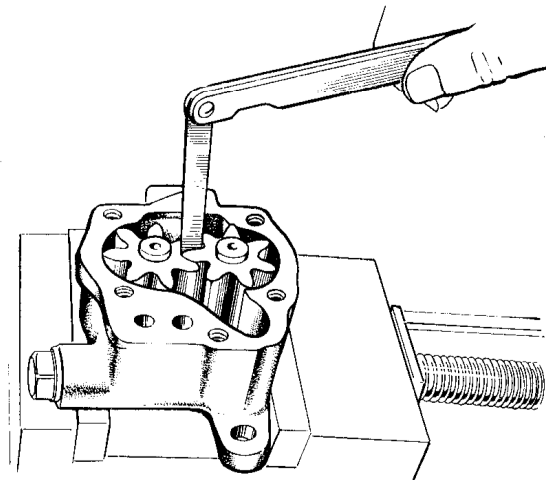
Проверка зазора между рабочими поверхностями зубьев в зацеплении шестерен
